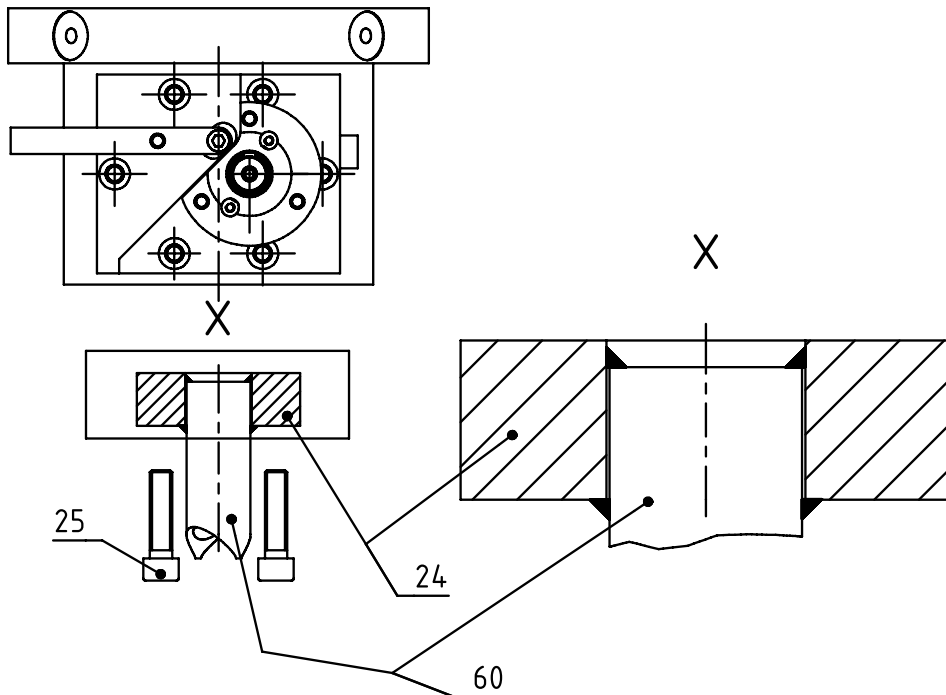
Сварка трубопровода на напорной 60 стороне с фланцем 24 продукта.
